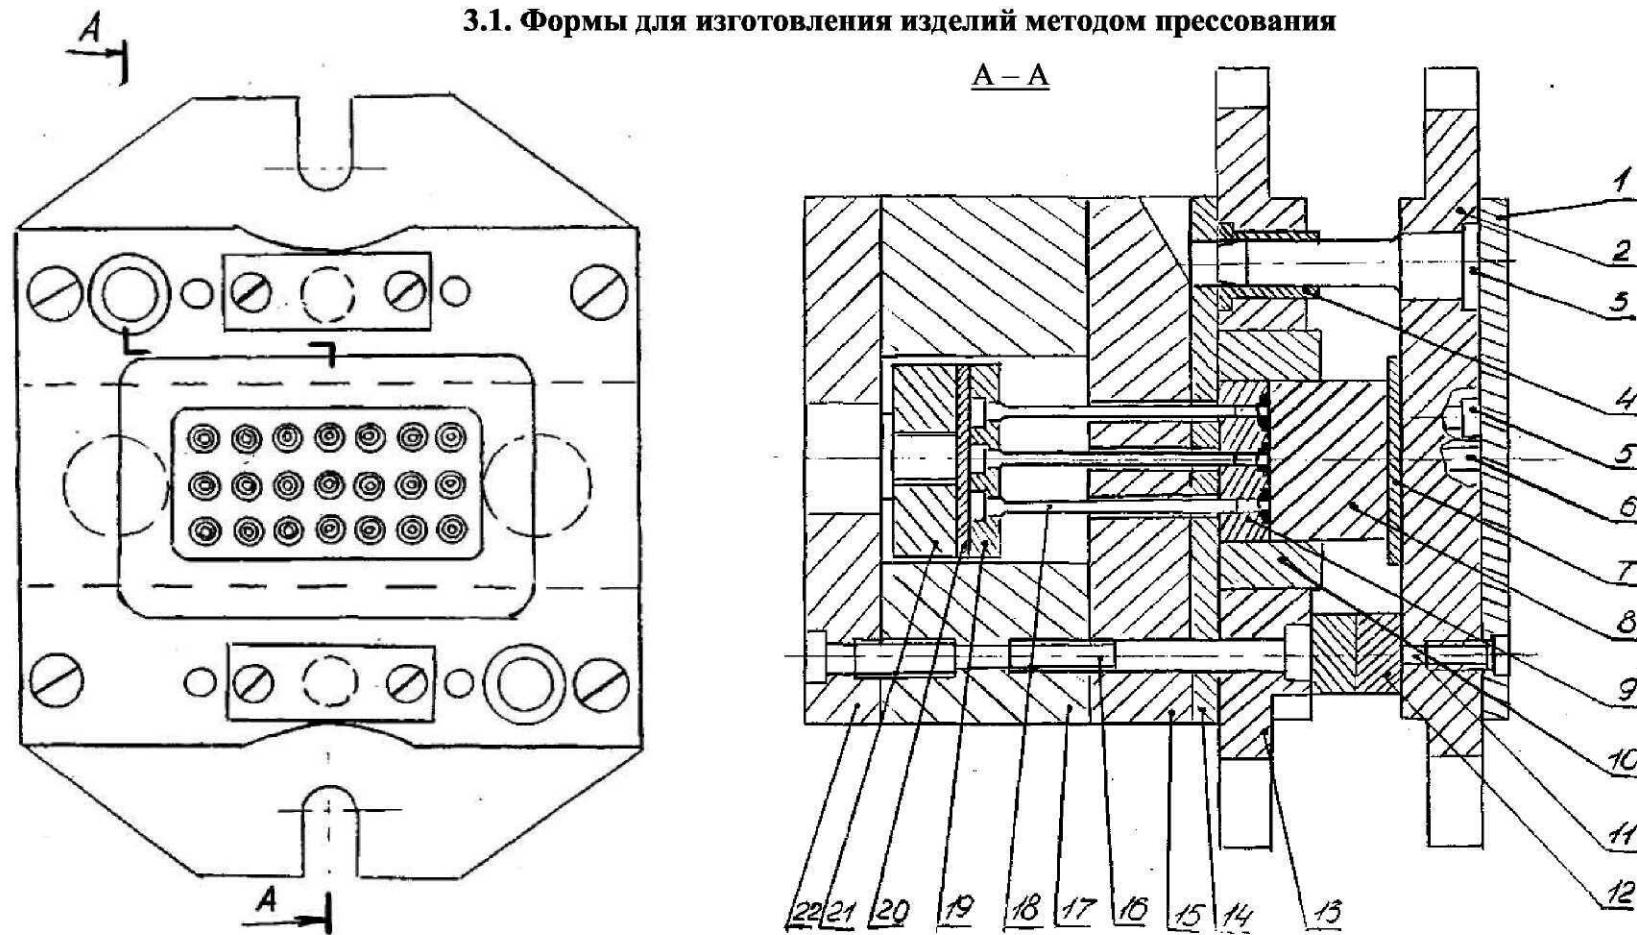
Пресс-форма для изготовления деталей методом прессования:
